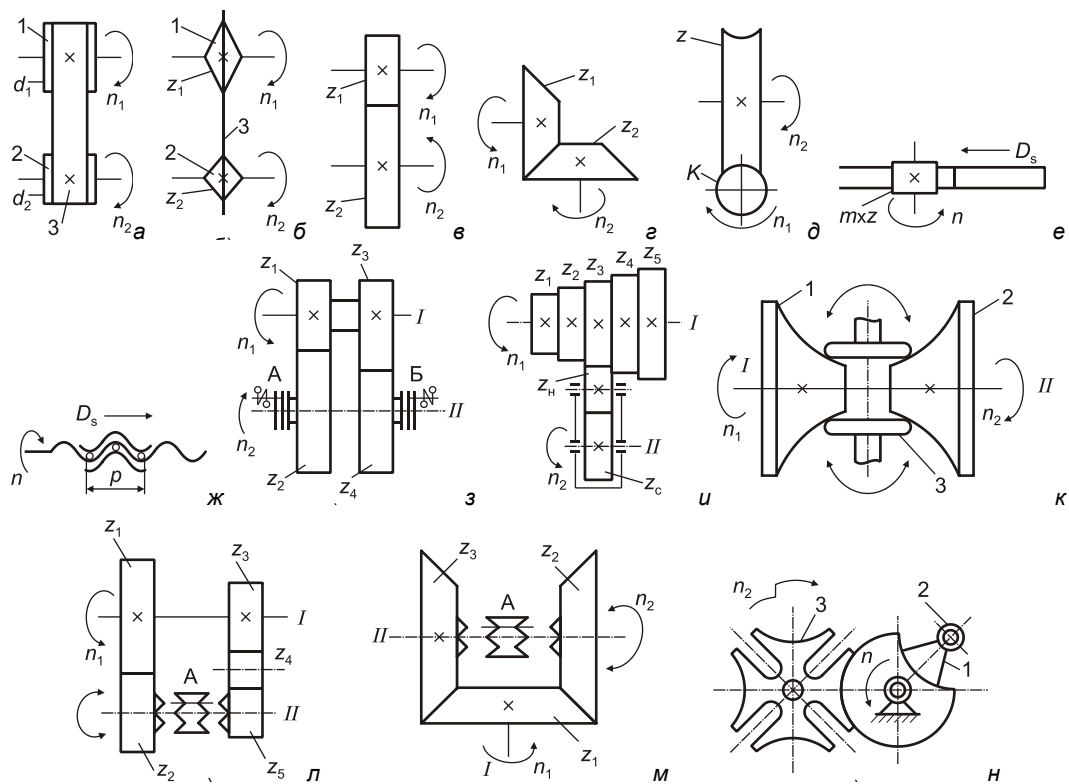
Схематическое изображение передач: а — ременная; б — цепная; в — зубчатая цилиндрическая; г — коническая; д — червячная; е — реечная; ж — "винт-гайка"; з-к — механизмы для изменения скорости; л, м — механизмы для изменения направления; н — механизм для осуществления периодических движений
